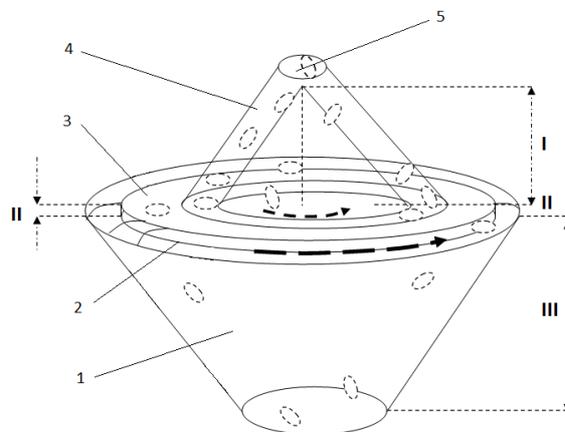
Схема корпуса скарификатора с указанием рабочих органов: 1 – приемник (бункер), 2 – вращающийся диск (ротор), 3 – неподвижный диск (крышка), 4 – вращающийся конус, 5 – семяпровод.
